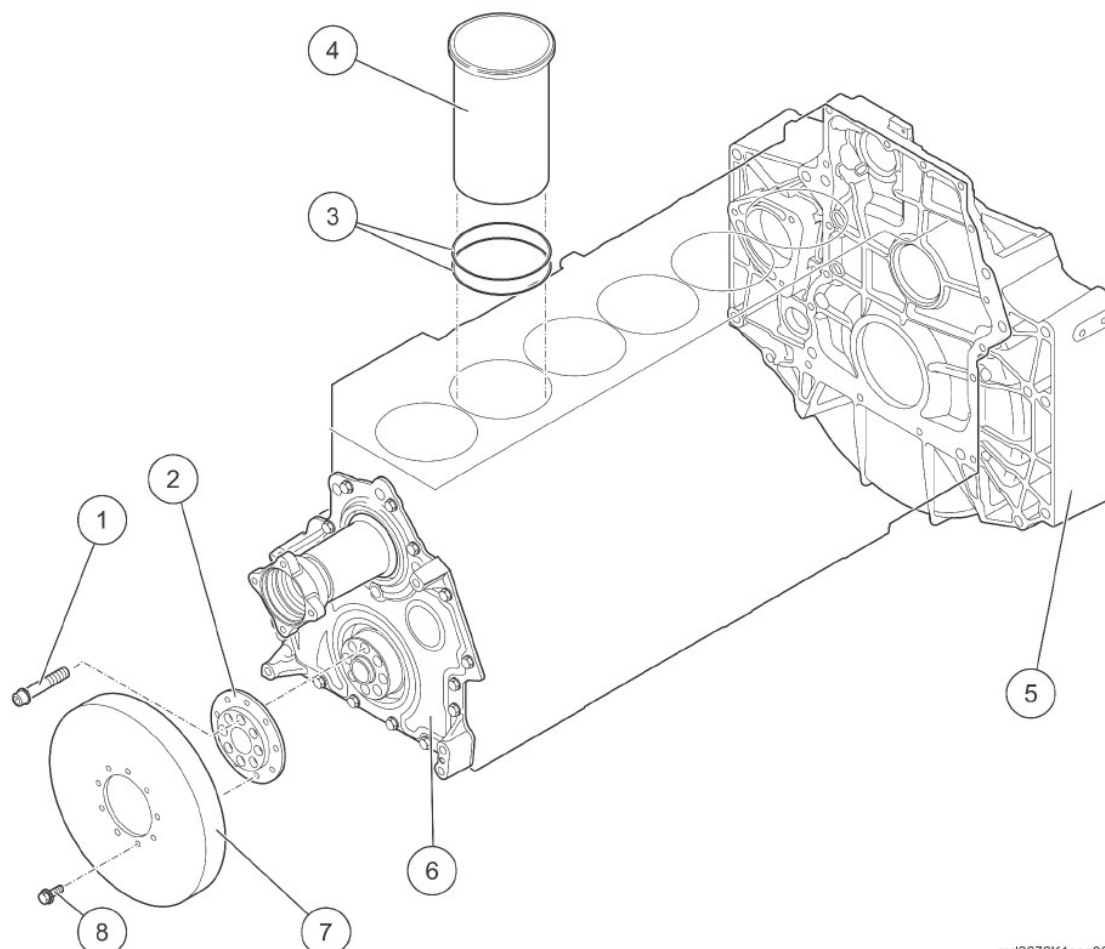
Монтажные детали на комплекте коробки коленчатого вала
